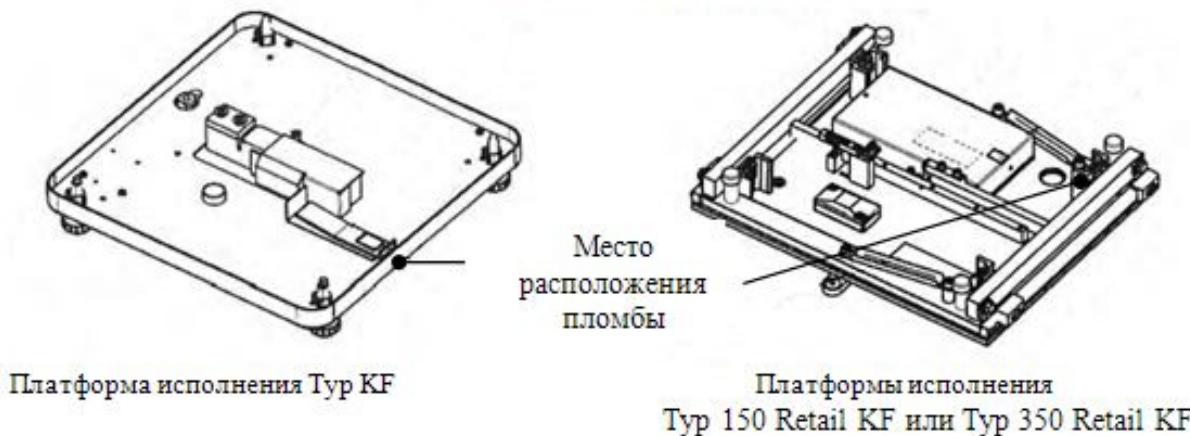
Схема пломбировки ГПУ исполнений Typ KF, Typ 150 Retail KF или Typ 350 Retail KF
